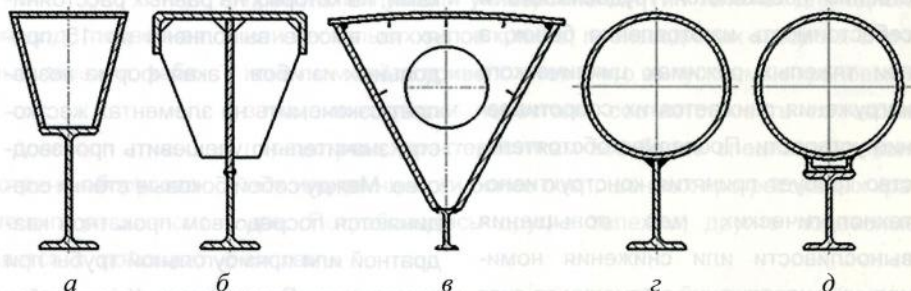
Поперечные сечения мостов с ездовыми балками из листовых и профильных элементов: а – трапецевидное; б – открытого профиля; в – треугольное; г – трубчатое с тавровым монорейсом; д – трубчатое с креплением двутавровой балки через швеллер
